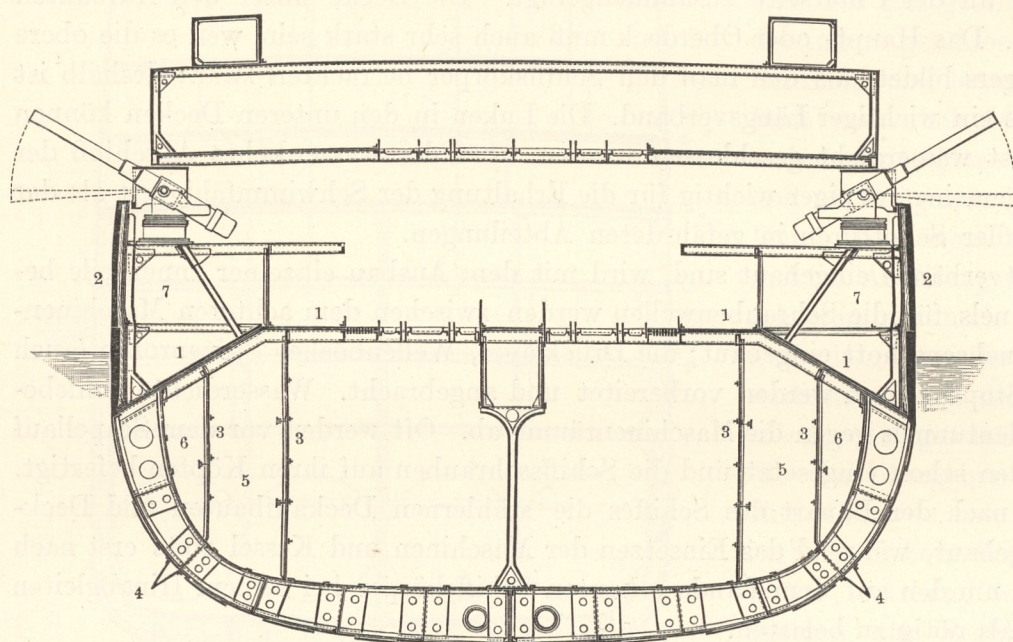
Hauptspant eines Linienschiffes (1 Panzerdeck, 2 Panzergürtel, 3 Längsschotte, 4 Schlingerkiel, 5 innerer Wallgang, 6 äußerer Wallgang, 7 Kofferdamm).
